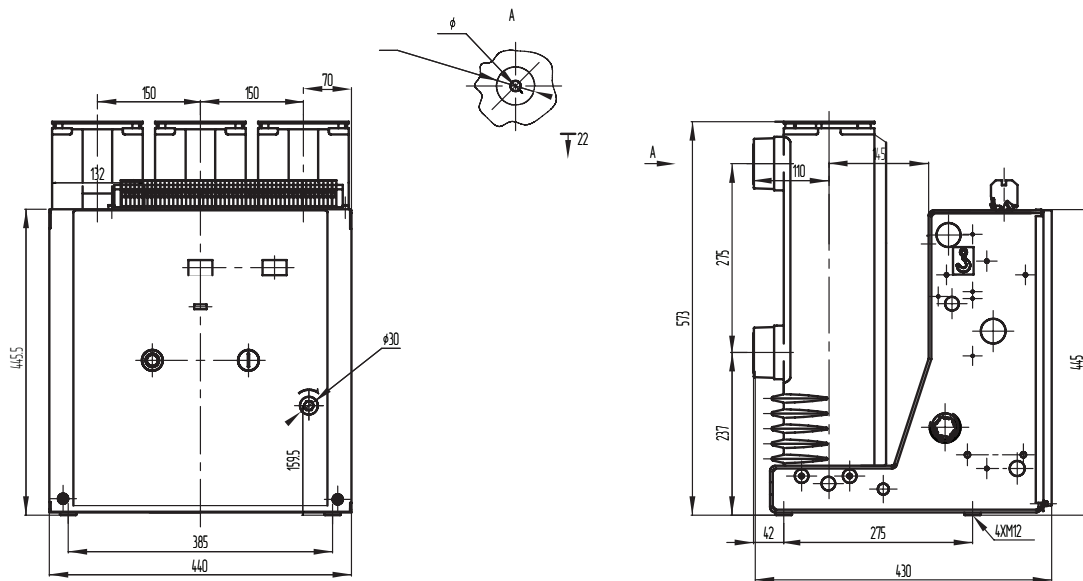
Габаритный размер выключателя ВВ стационарного исполнения для ячейки шириной 800 мм
